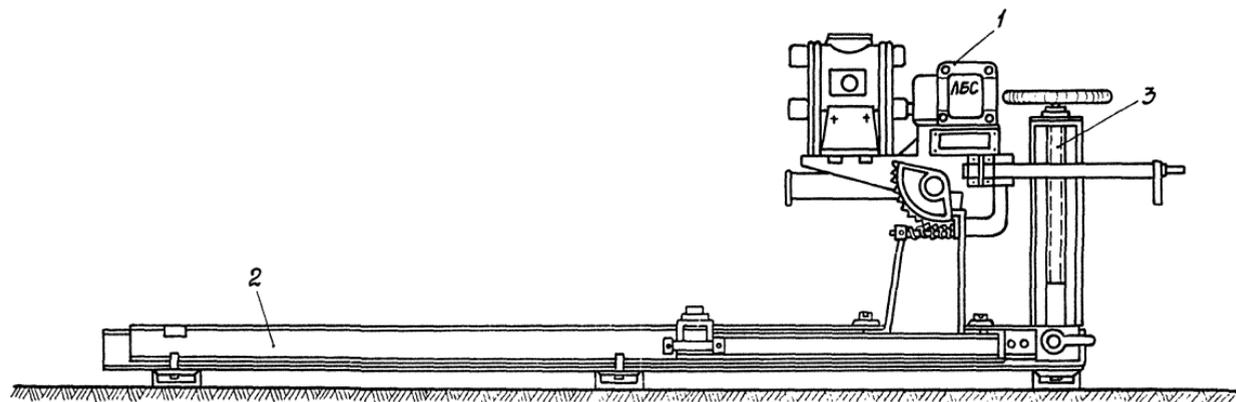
Подъемно-установочное приспособление для бурового станка.
